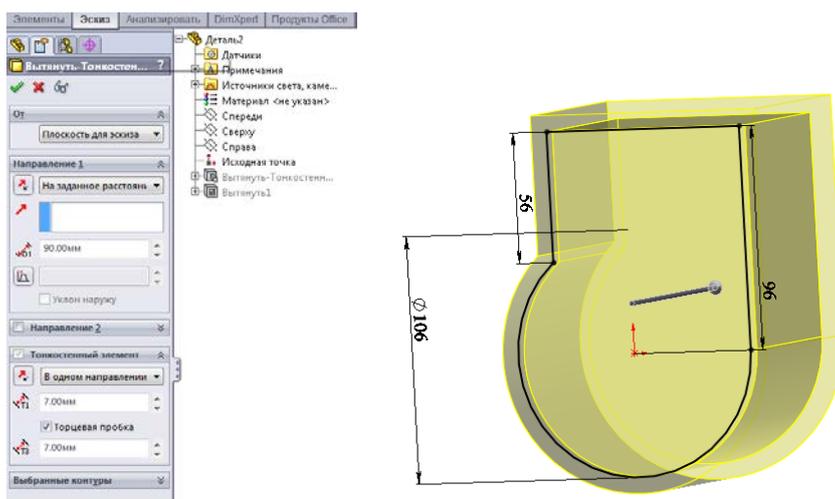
Получение заготовки главной части корпуса редуктора как тонкостенный элемент
